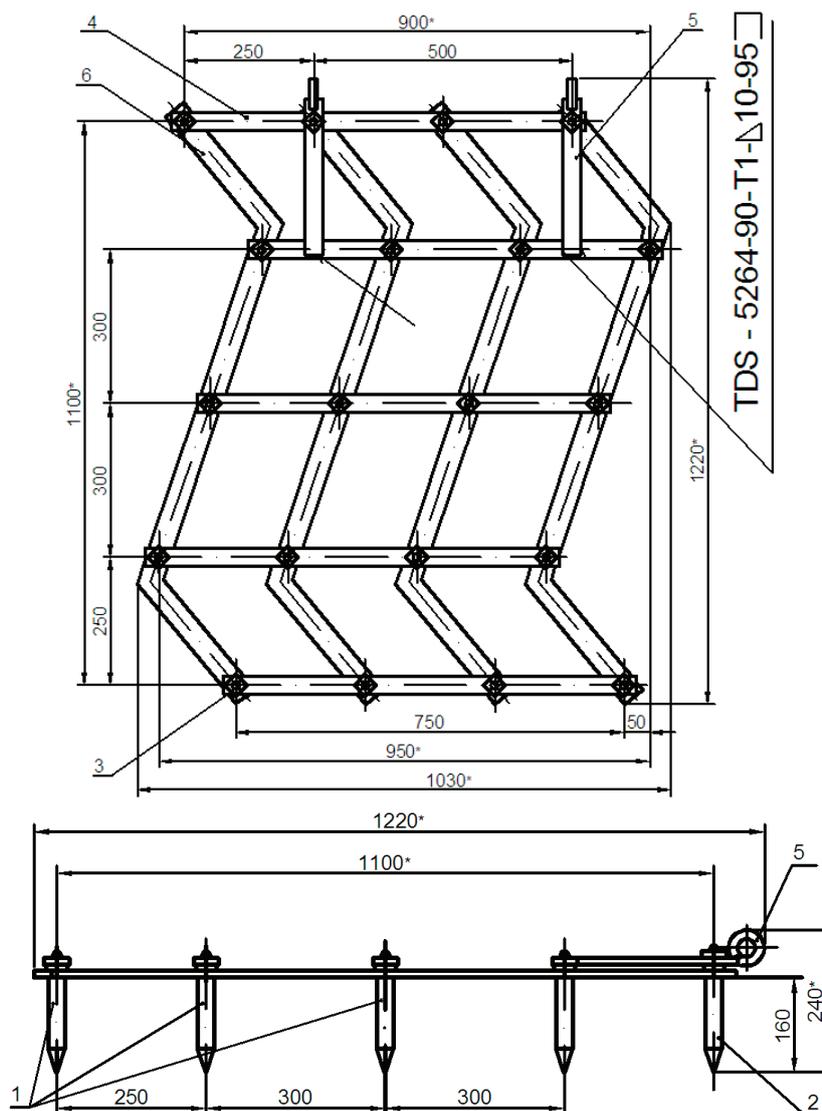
Основные размеры двадцати зубовой бороны: 1 — вид зуба бороны № 1; 2 — вид зуба бороны № 2; 3 — гайка зуба бороны; 4 — горизонтальная планка; 5 — кольцевая планка; 6 — горизонтальная линия (z)
